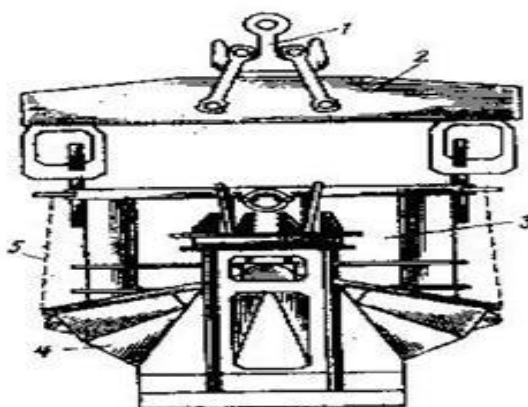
Загрузочная бадья грейферного типа. 1 – крюк; 2 – траверса; 3 – корпус; 4 – челюсти; 5 – канаты
